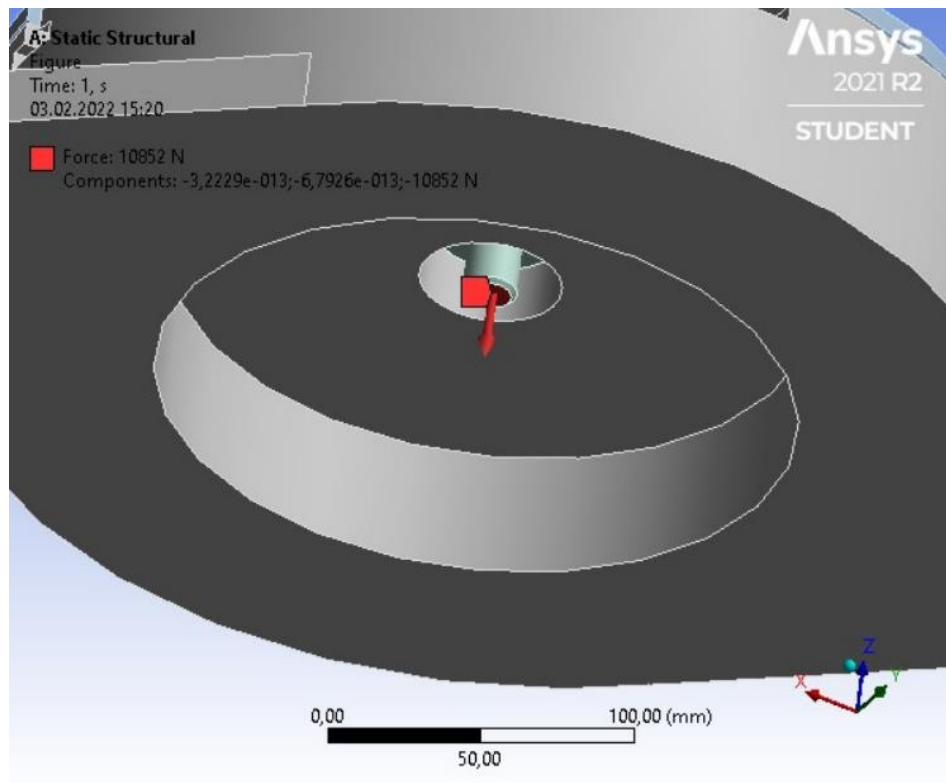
Дія зусилля з боку приводу затискання заготовки
